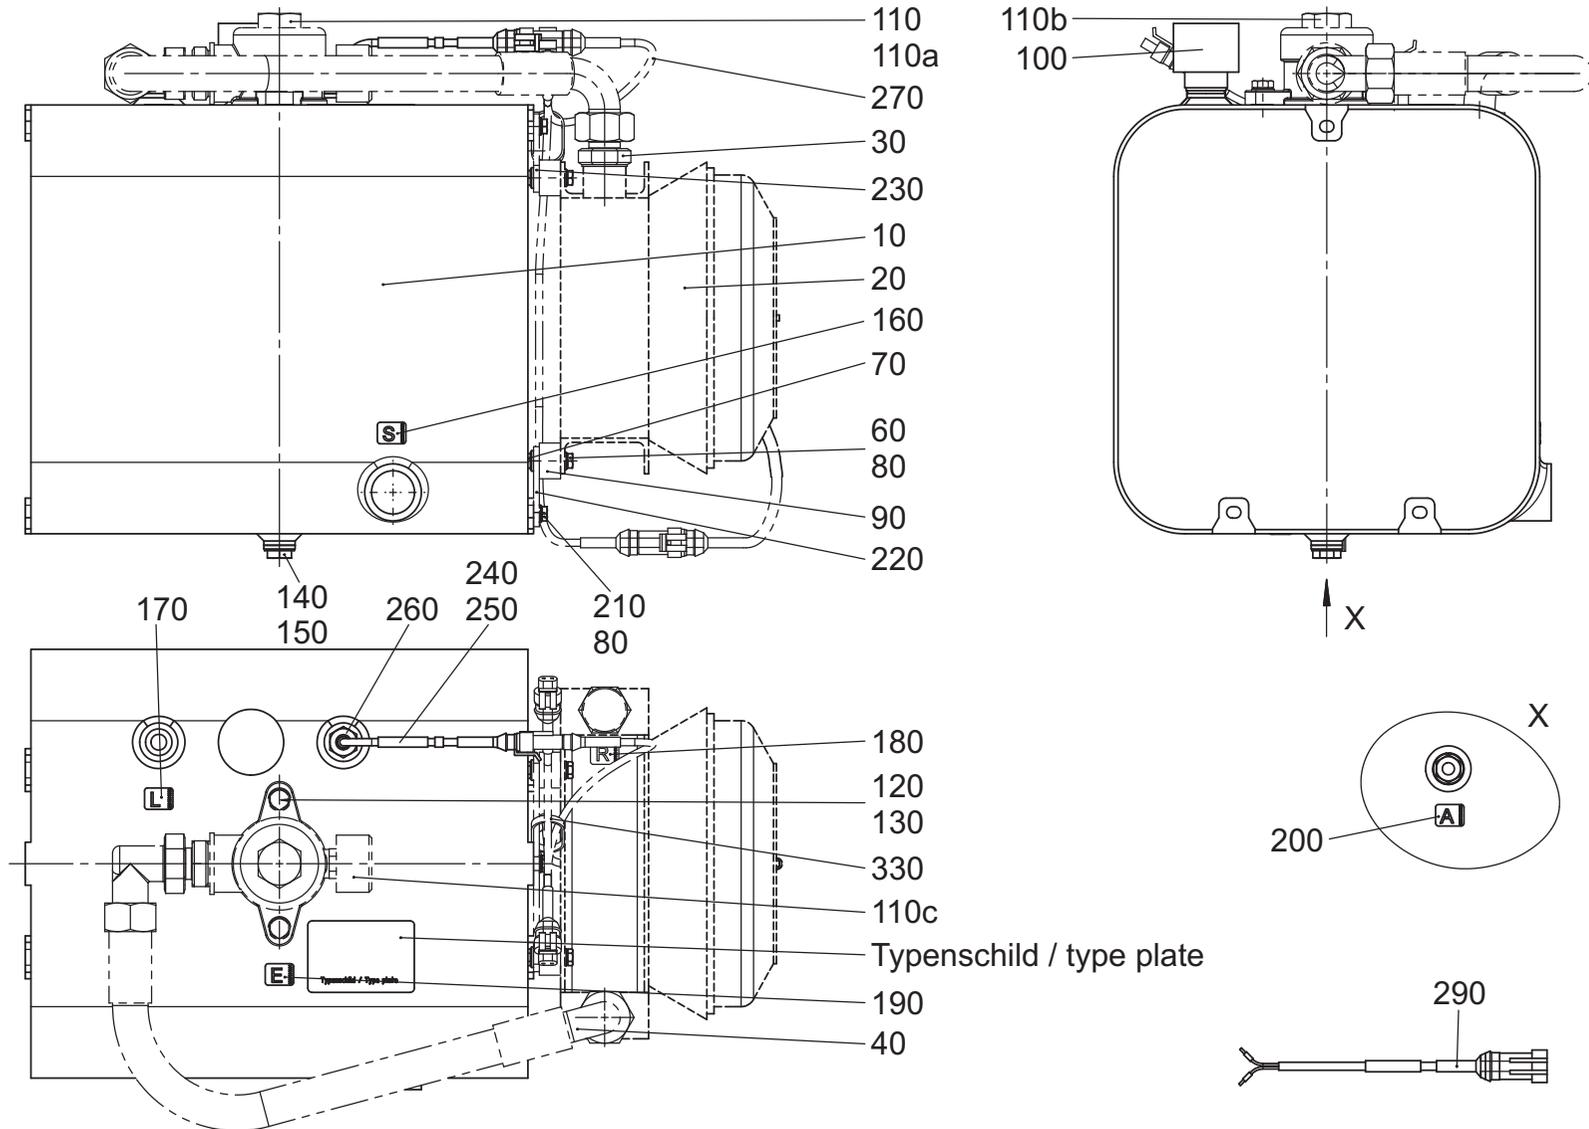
Ersatzteile der Öltanks mit Kühler sowie mit Kühler und Füllstandsmesser
